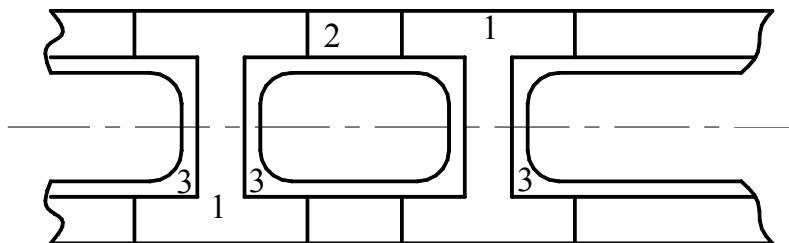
Сварные стыки и кромка настила палубы и выреза
